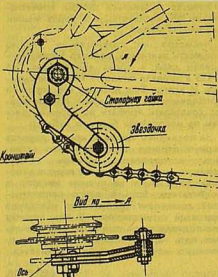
Устройство для регулировки натяжной цепи ножного привода.
